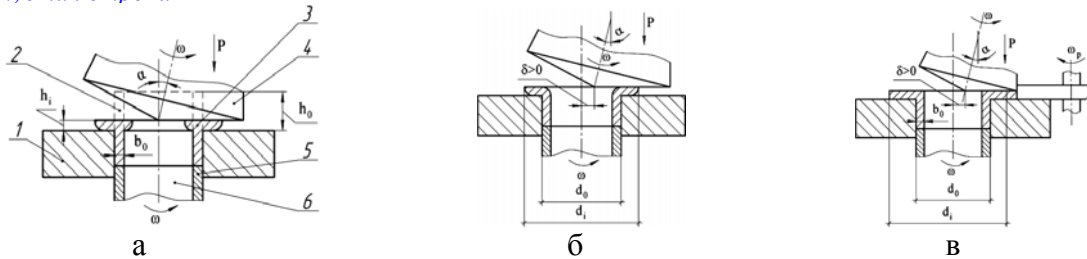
Схемы высадки раскаткой буртов (1 – матрица; 2 – заготовка; 3 – изделие; 4 – валок; 5 – выталкиватель; 6 – оправка):
